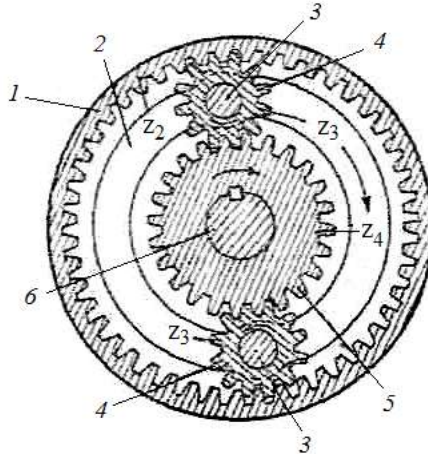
Планетарна передача з внутрішнім зачепленням
